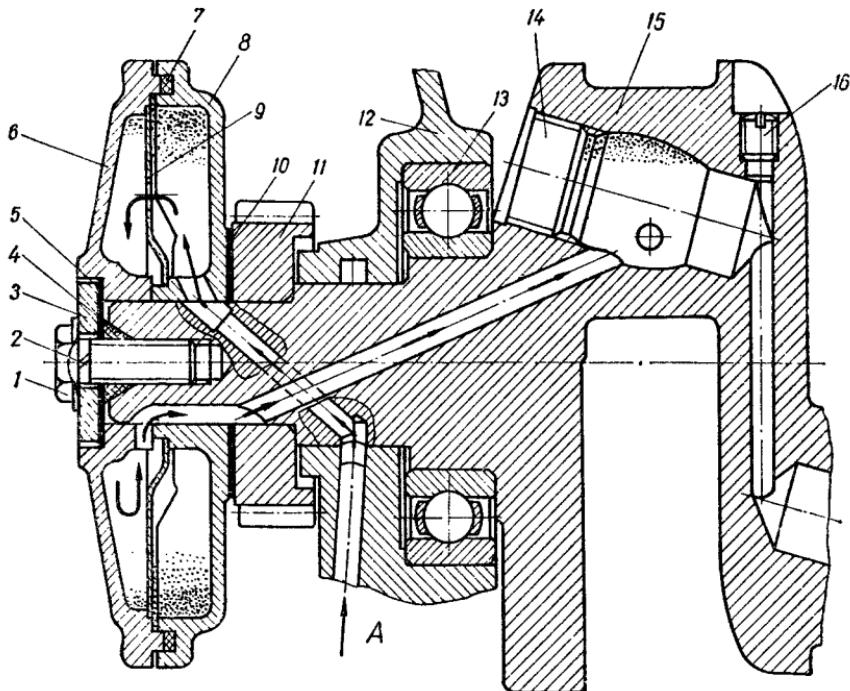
Центрифуга и передний коренной шарикоподшипник:
